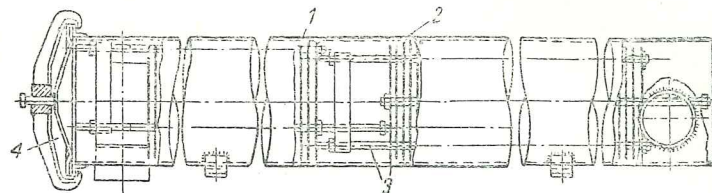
Схема очистителя-охладителя установки ЗИС для автомобиля ЗИС-21
